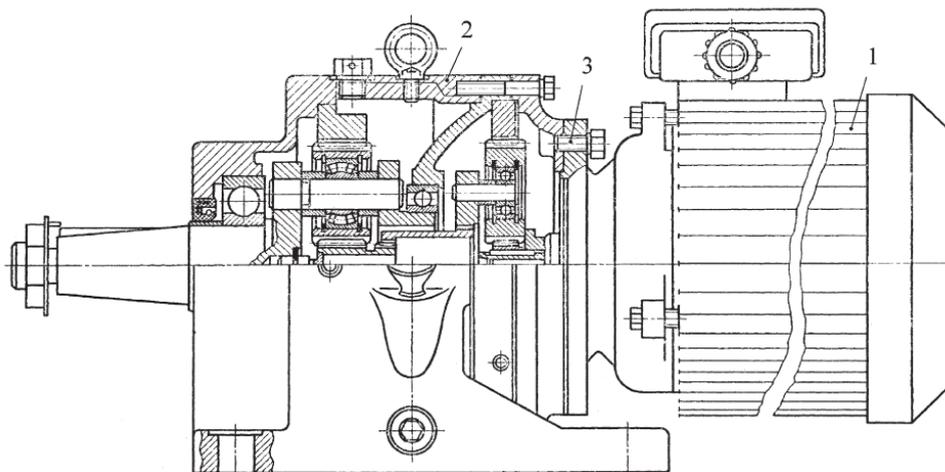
Планетарный двухступенчатый мотор-редуктор
